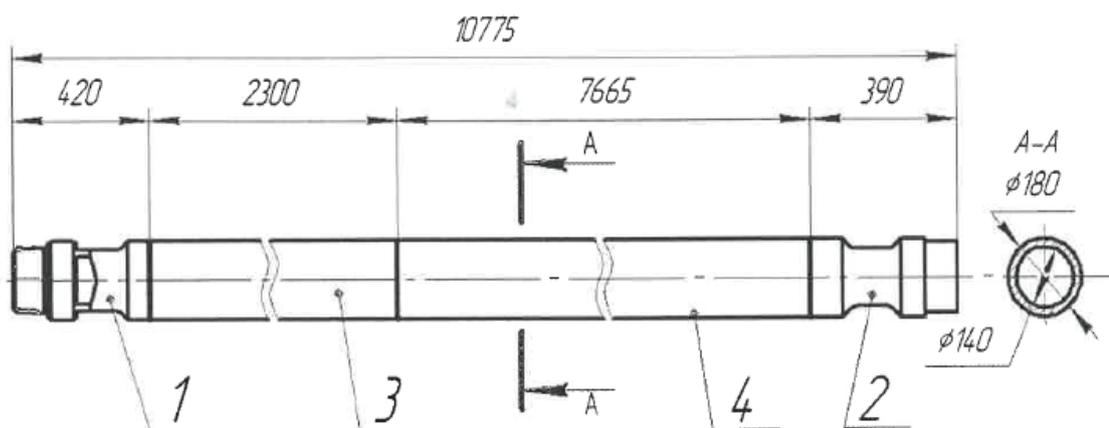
эскиз технология сборки и сварка буровой штанги.
